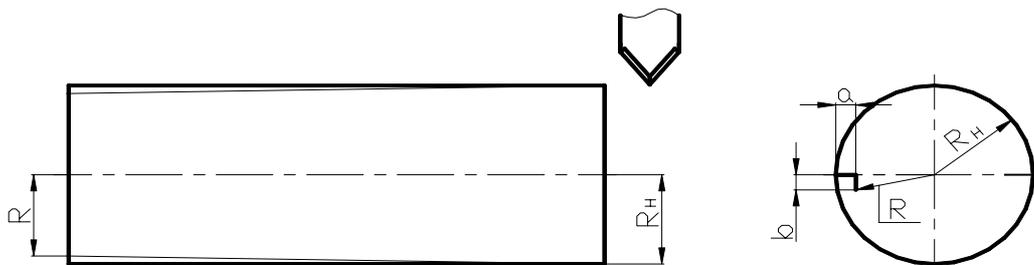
Форма поверхности при односторонней токарной обработке (резец расположен за линией центров)
